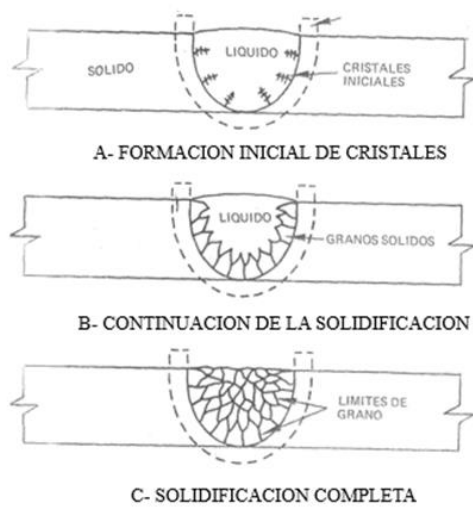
Etapas de la solidificación de un metal en la soldadura.
